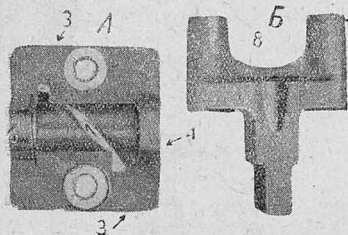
А—кондуктор-рамка для нарезки канавок в подшипниках. Б—державка, употребляемая при нарезке канавок в крышках подшипников
